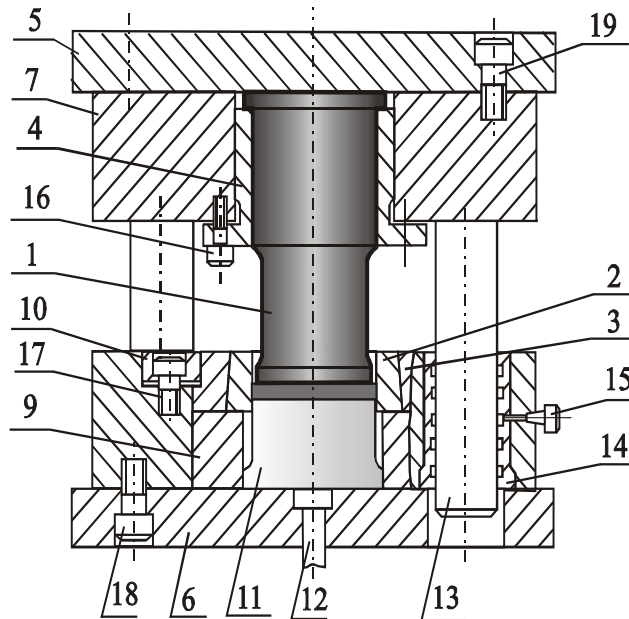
Схема штампа для осадки квадратної заготовки:
